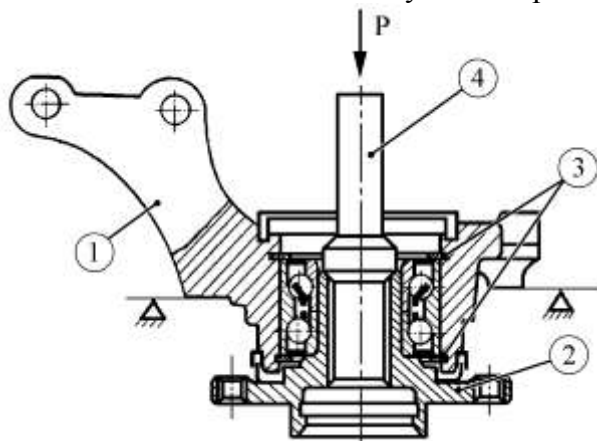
Выпрессовка ступицы переднего колеса из поворотного кулака:
